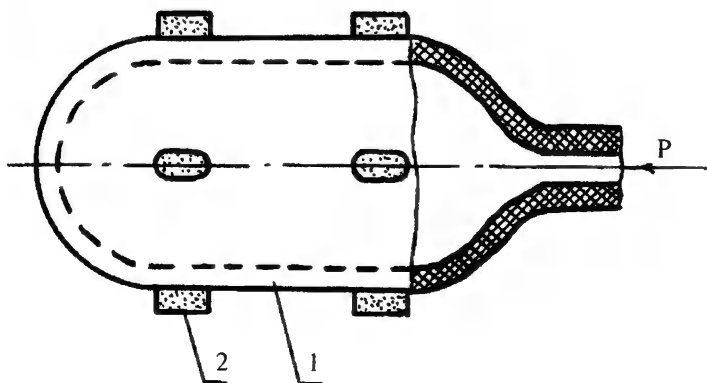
Пневматическая хонинговальная головка: 1 - корпус эластичный, 2 - брусок
